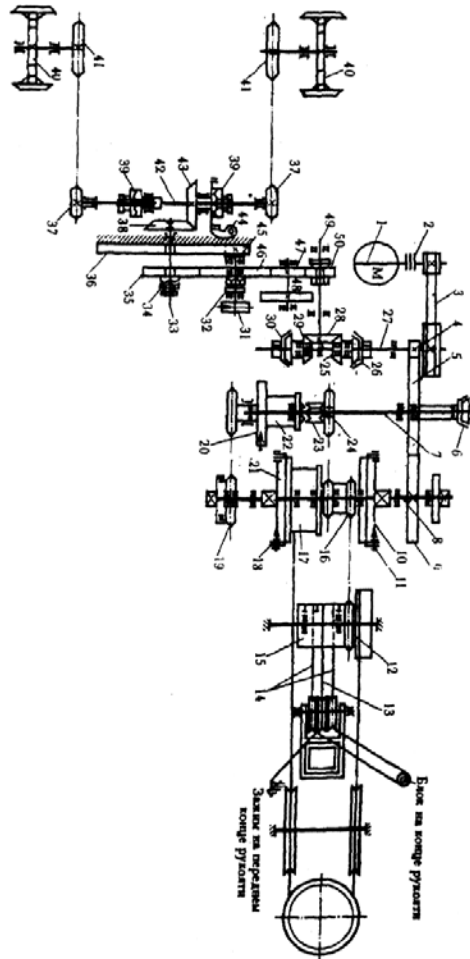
Кинематическая схема экскаваторов Э-652Б, ЭО-4111В и ЭО-4112 с прямой лопатой:
